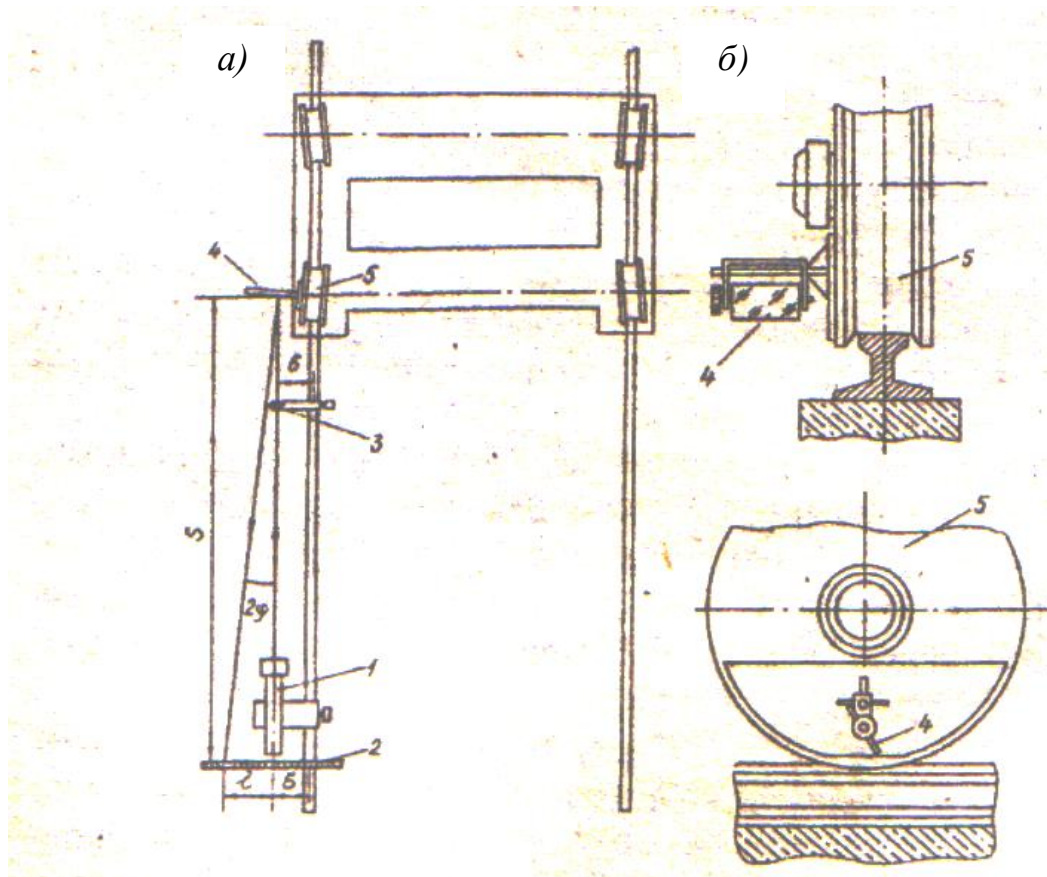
Устройство для контроля углов перекоса колёс (а) и приспособление для крепления зеркала (б)
